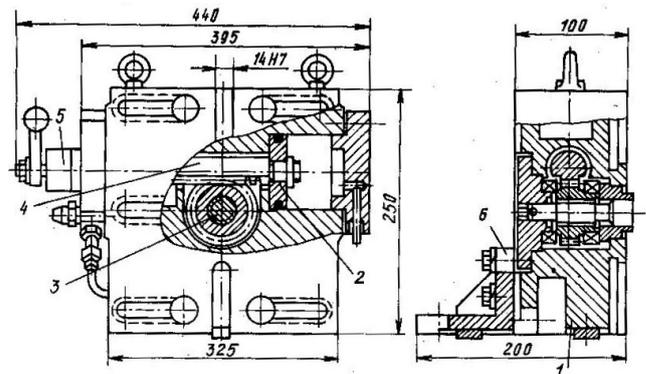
Схема пневмомеханической наладочной кантуемой стойки
